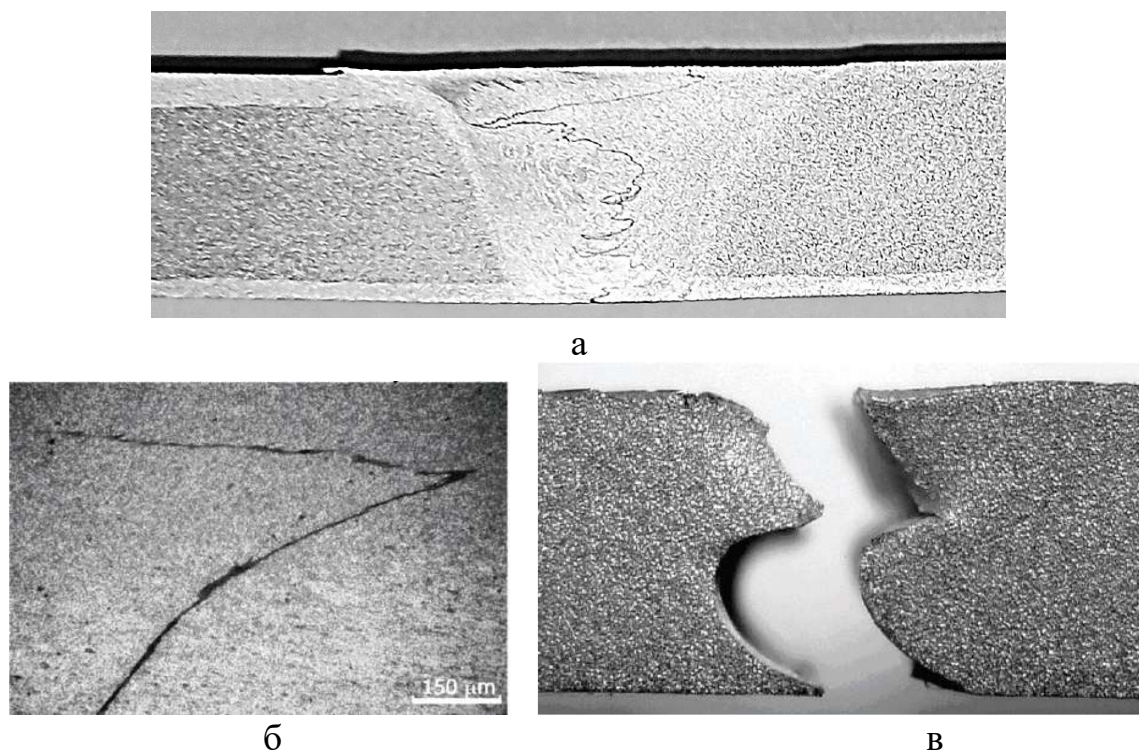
Линия стыка на поперечном сечении сварного шва сплава 6082Т6 (а) и фрагмент разрушенного образца (б); в – разрушение материала по полосам луковичной структуры
